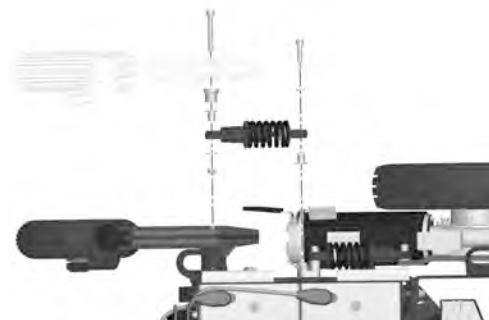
Anbringen oder Ausbauen des hinteren Stoßdämpfers.
